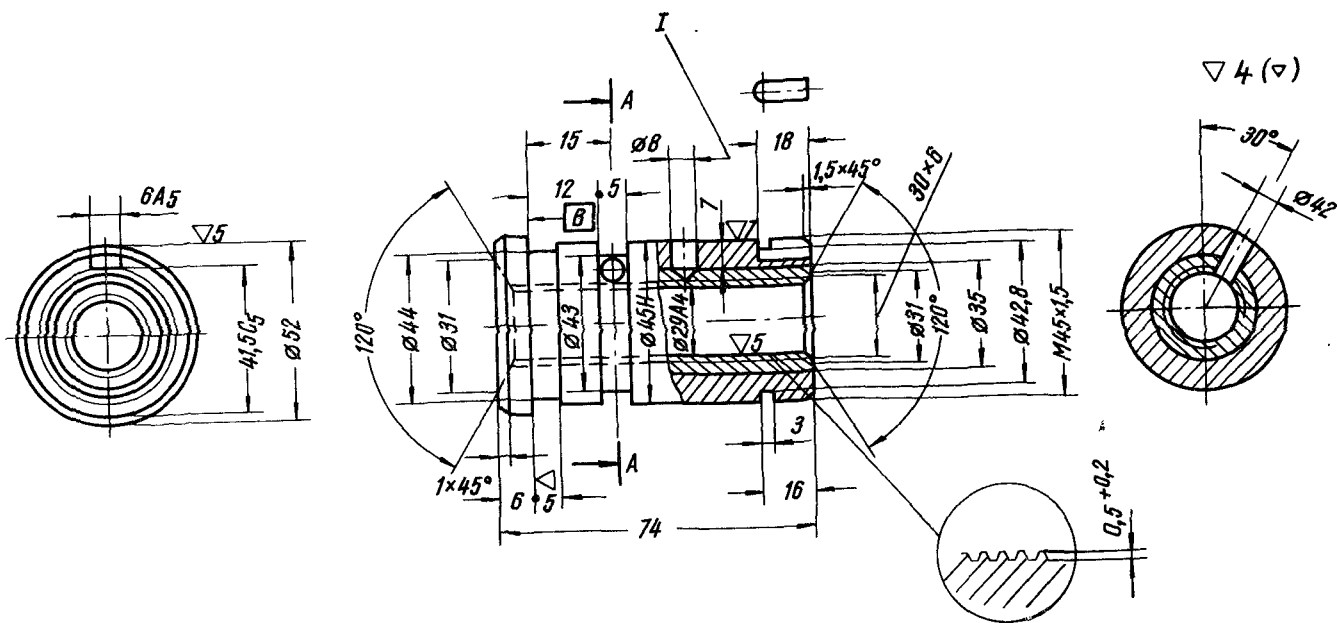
Гайка биметаллическая. Деталь 6M82-7-103
